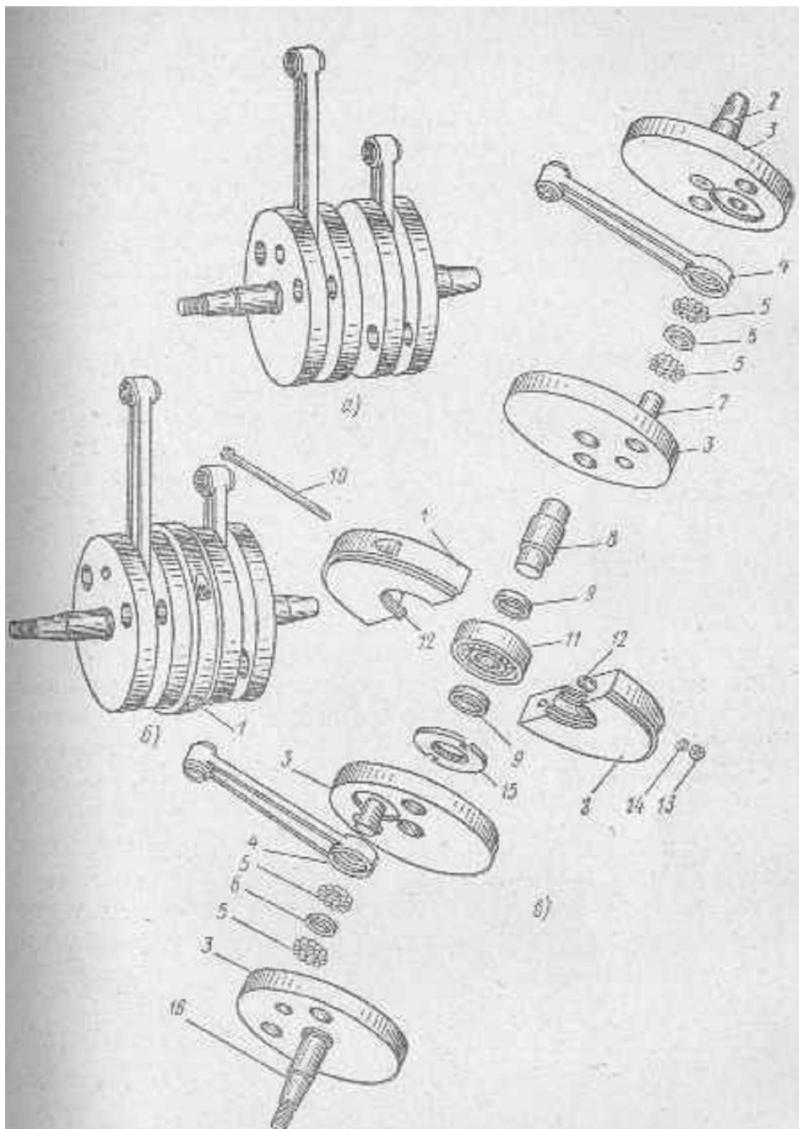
Коленчатый вал двухцилиндрового двигателя мотоцикла ЯВА-350:
